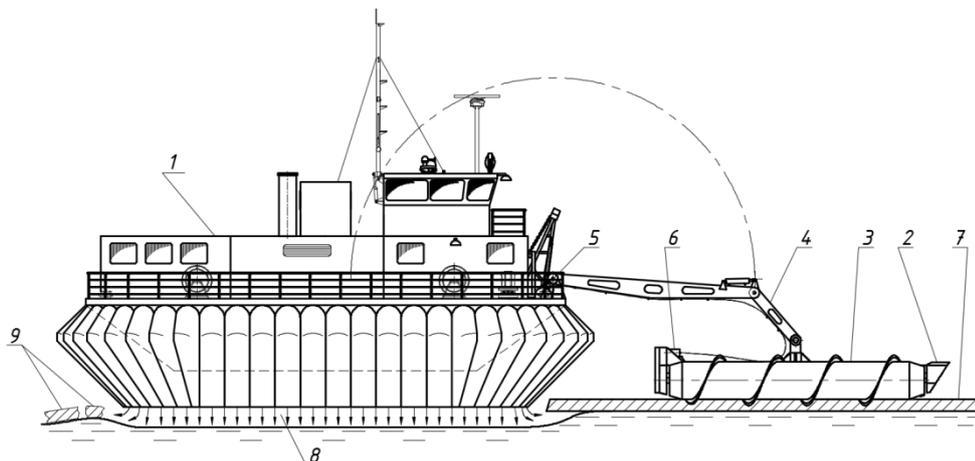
Схема движения ЛППВ с роторно-винтовым движителем
